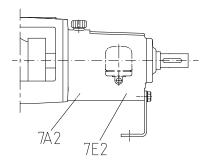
Anschlüsse bei Ausführung mit kühlbarem Lagerträger
